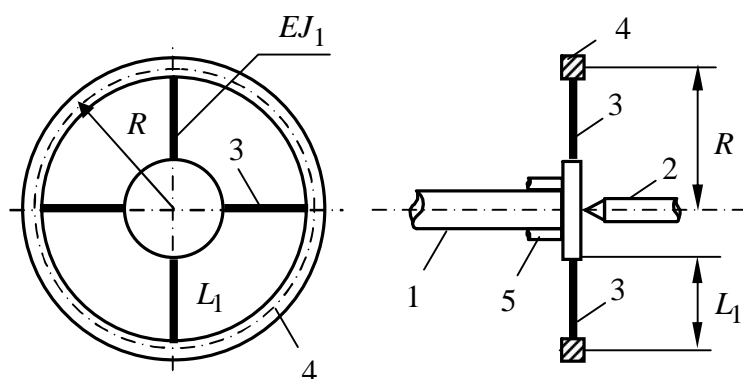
Схема динамического гасителя изгибных колебаний нежесткой заготовки: 1 – нежесткая заготовка; 2 – центр; 3 – упругие элементы гасителя; 4 – кольцо массы  $m_2$ ; 5 – фиксаторы.
